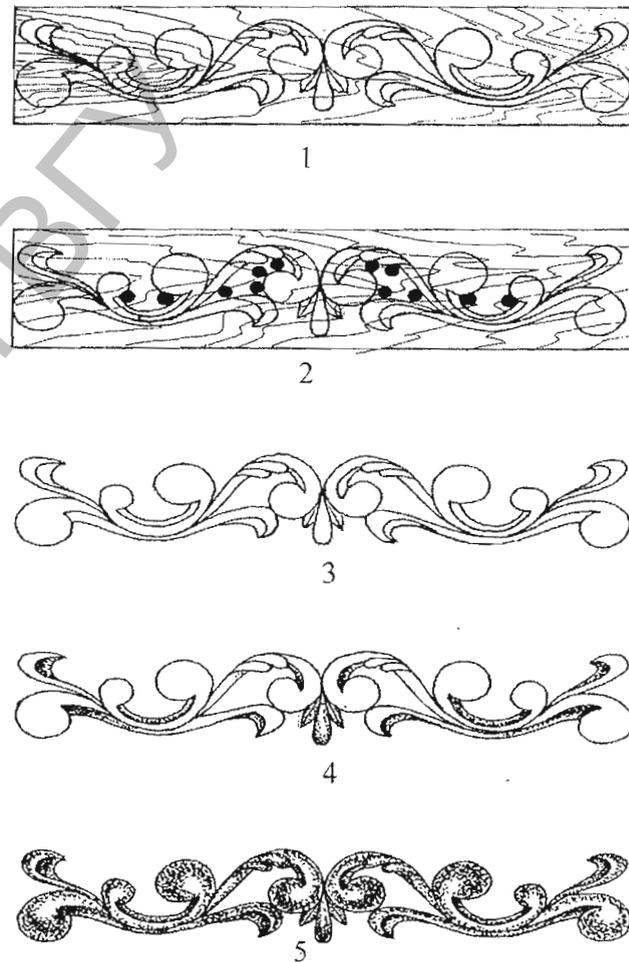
Последовательность выполнения накладных рельефных элементов рамы: 1 – перевод рисунка; 2 – сверление; 3 – выпиливание; 4 – резьба углублений; 5 – резьба выпуклостей.
